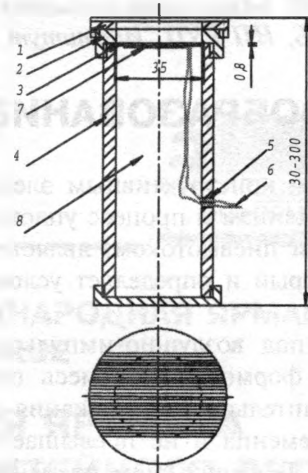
Общий вид датчика: 1 — крышка с прорезями; 2 — крышка прижимная; 3 — пластина; 4 — корпус; 5 — отверстие подвода проводов; 6 — провода; 7 — тензорезистор; 8 — полость датчика
